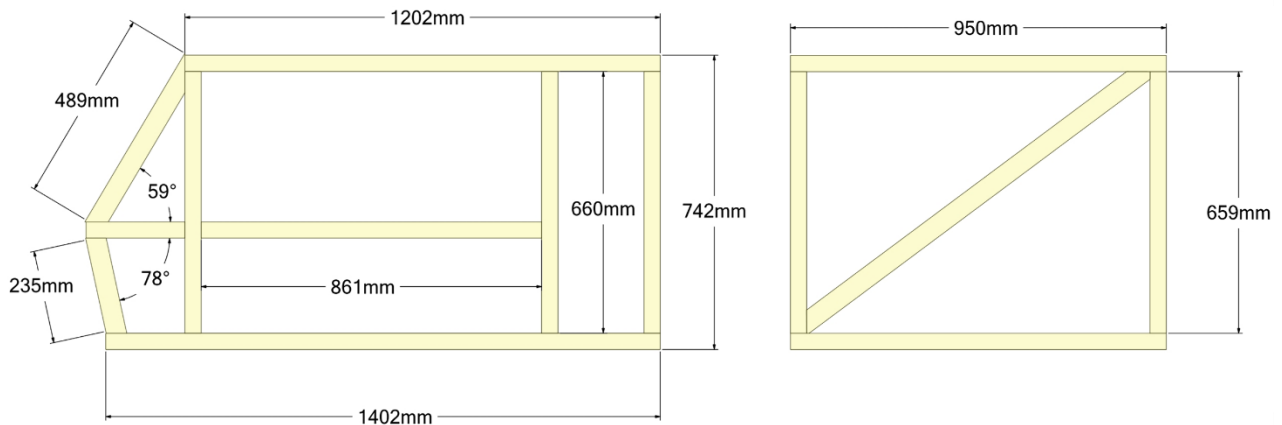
Geometría de los paneles laterales (izquierda) y paneles posteriores (derecha)
